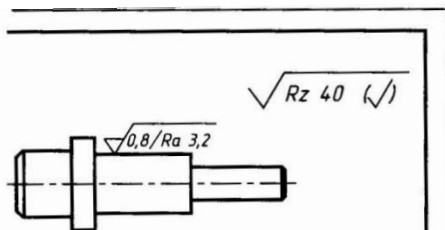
Простановка шероховатости поверхностей с разными значениями
